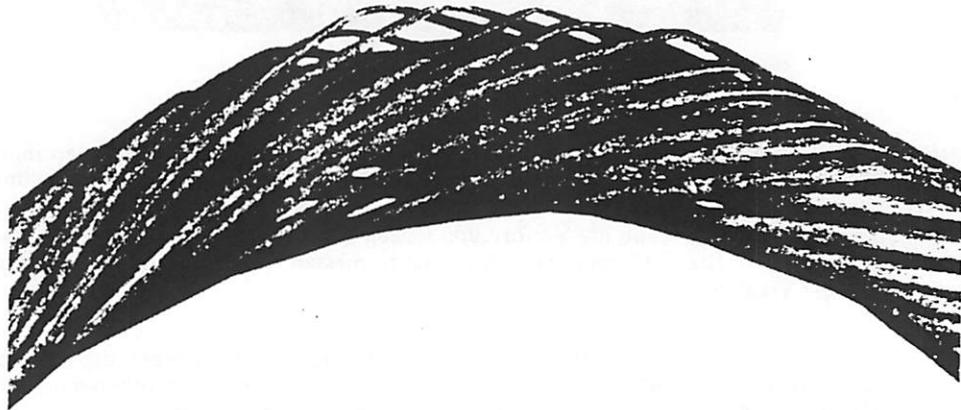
Drahtseil mit durch Korrosion und Abrieb gelockerten Drähten
